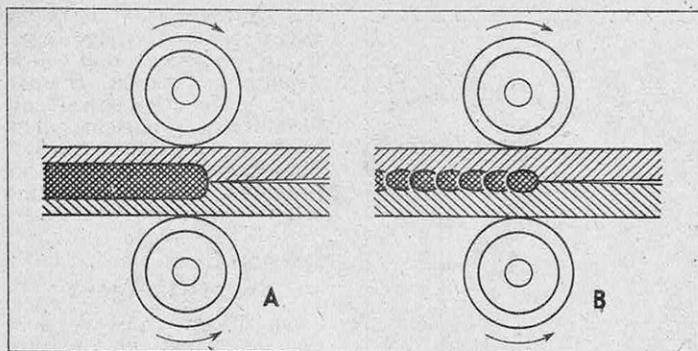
SOUDURE A LA MOLETTE
